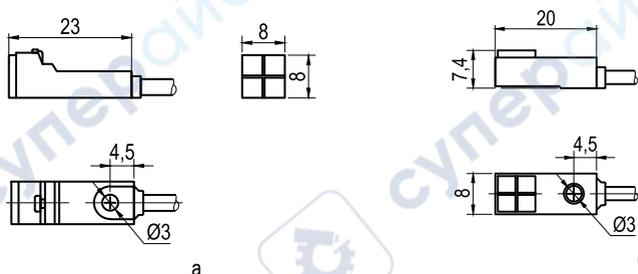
Габаритные и установочные размеры датчиков с шириной корпуса 8 мм
